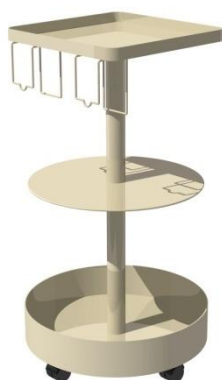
Carro de apoio à soldadura (vista isométrica).
